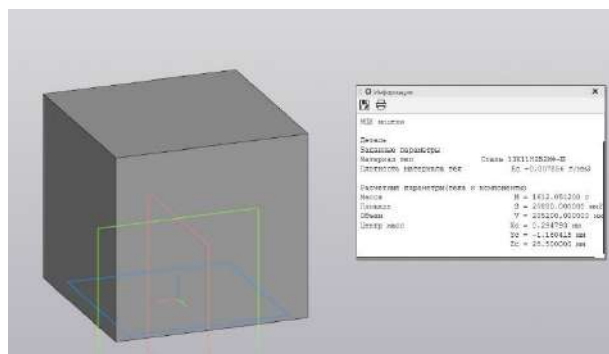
3D модель заготовки отриманої з каліброваного прокату квадратного перерізу
